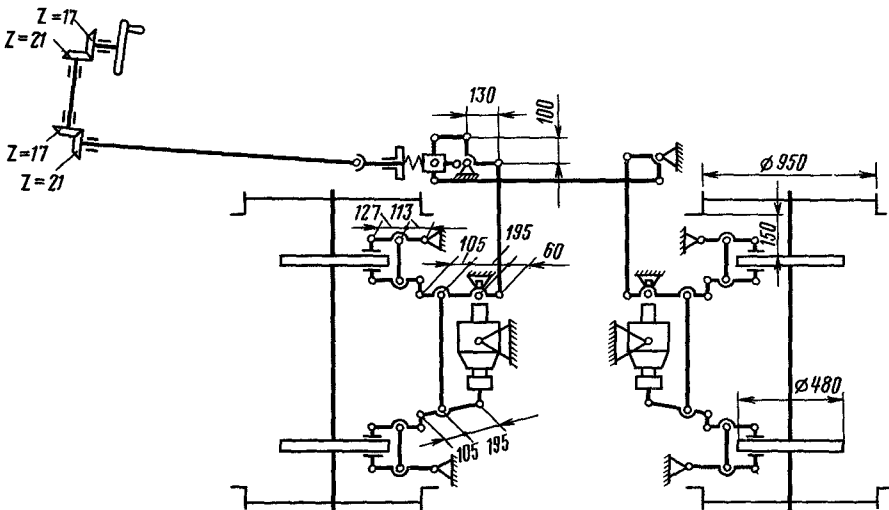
Схема рычажной передачи дискового тормоза пассажирского вагона
